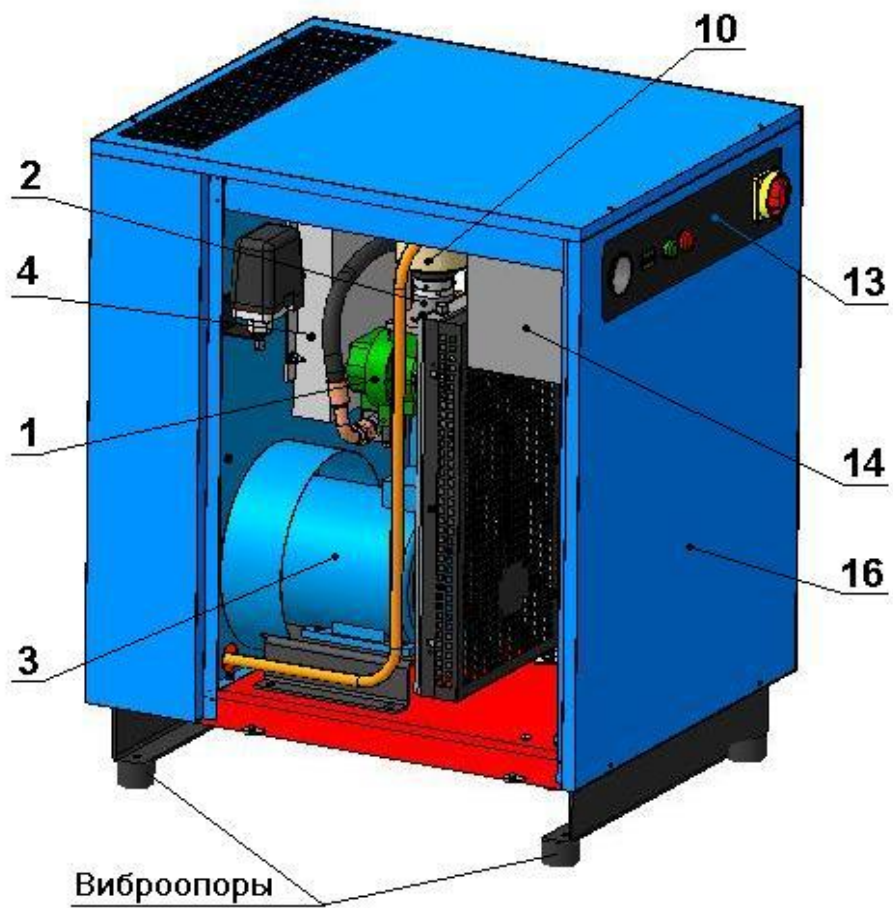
Общий вид компрессорной установки ВК5-..., ВК7-..., ВК10-...
